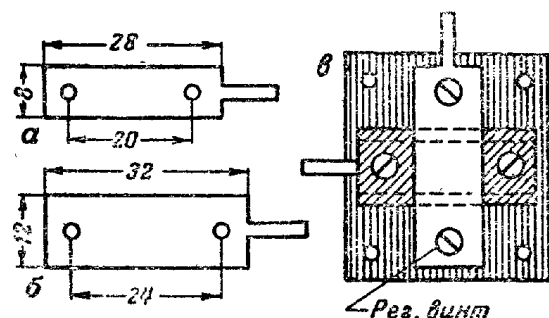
Устройство плоского подстроечного конденсатора: а — неподвижная пластина; б — подвижная пластина; в — собранный конденсатор.
